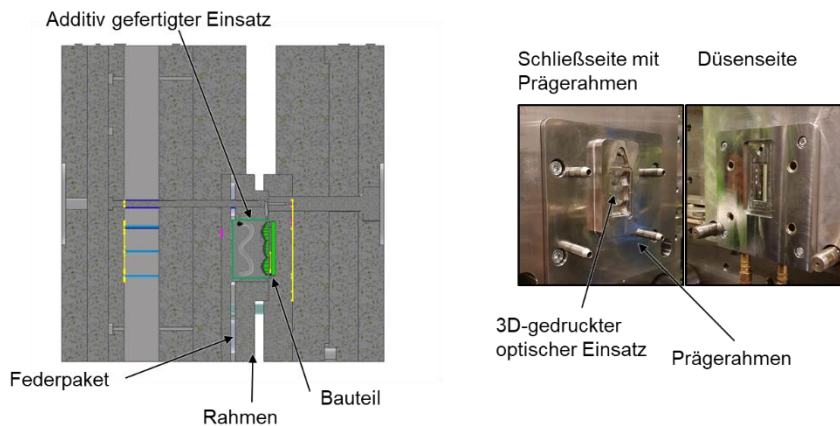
Werkzeugkonstruktion und montiertes Werkzeug in der Spritzgießmaschine
